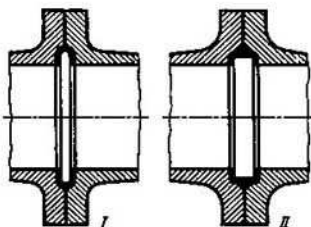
Empaquetaduras de manguito en las juntas de las tuberías
